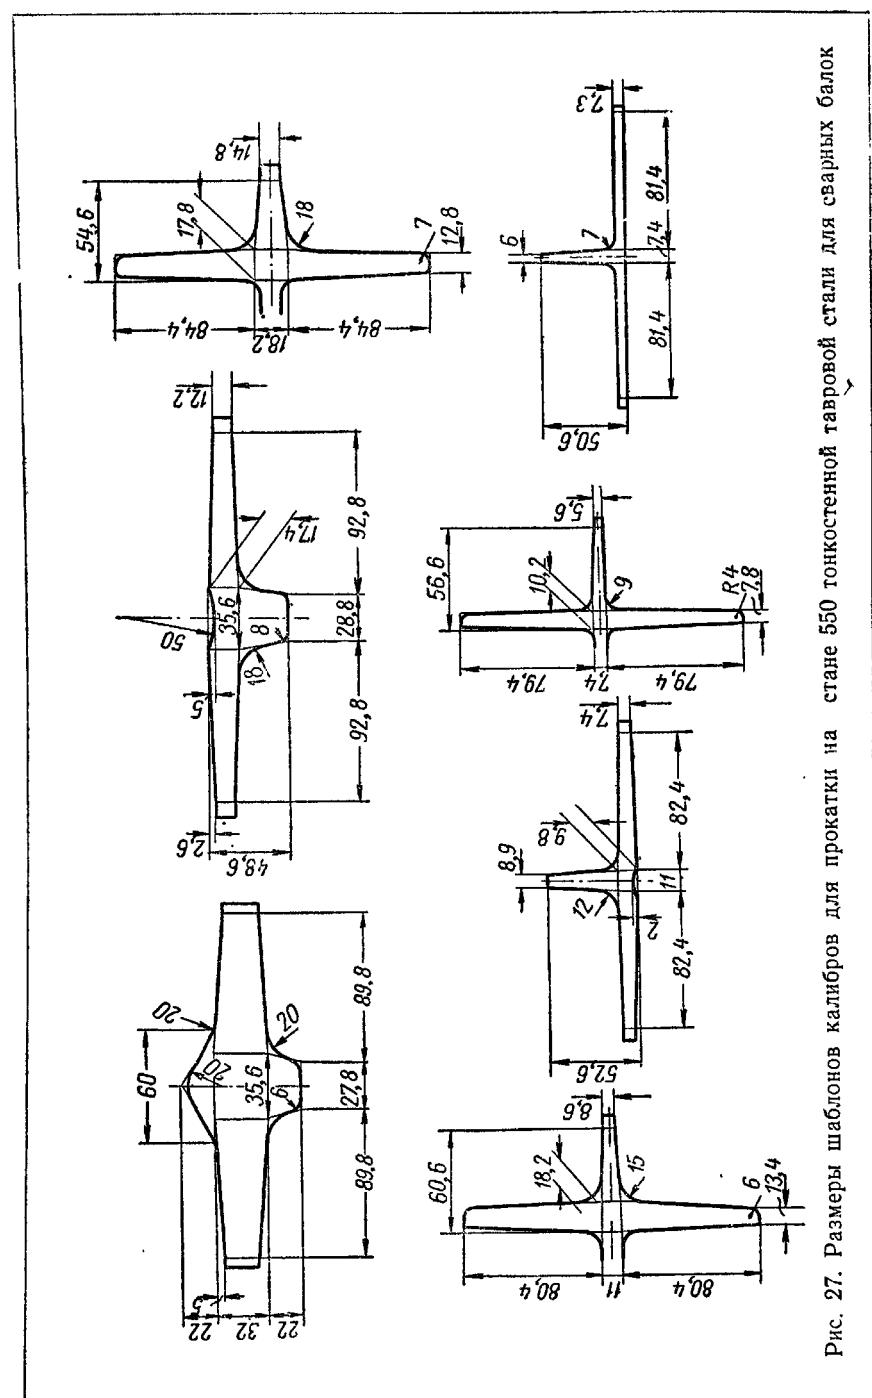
Размеры шаблонов калибров для прокатки на стане 550 тонкостенной тавровой стали для сварных балок
